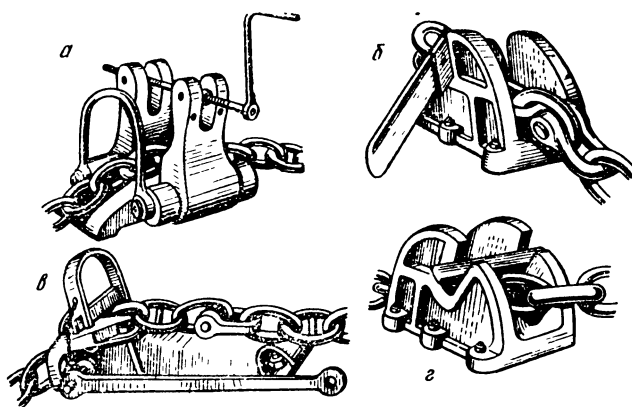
Стопоры: а — винтовой; б — стопор Легофа; в — с накидным палом
